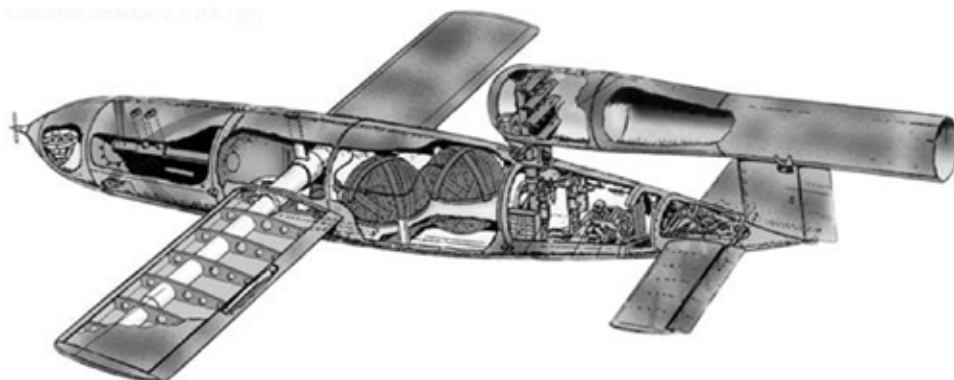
Pierwsze opublikowane zdjęcie V-1
